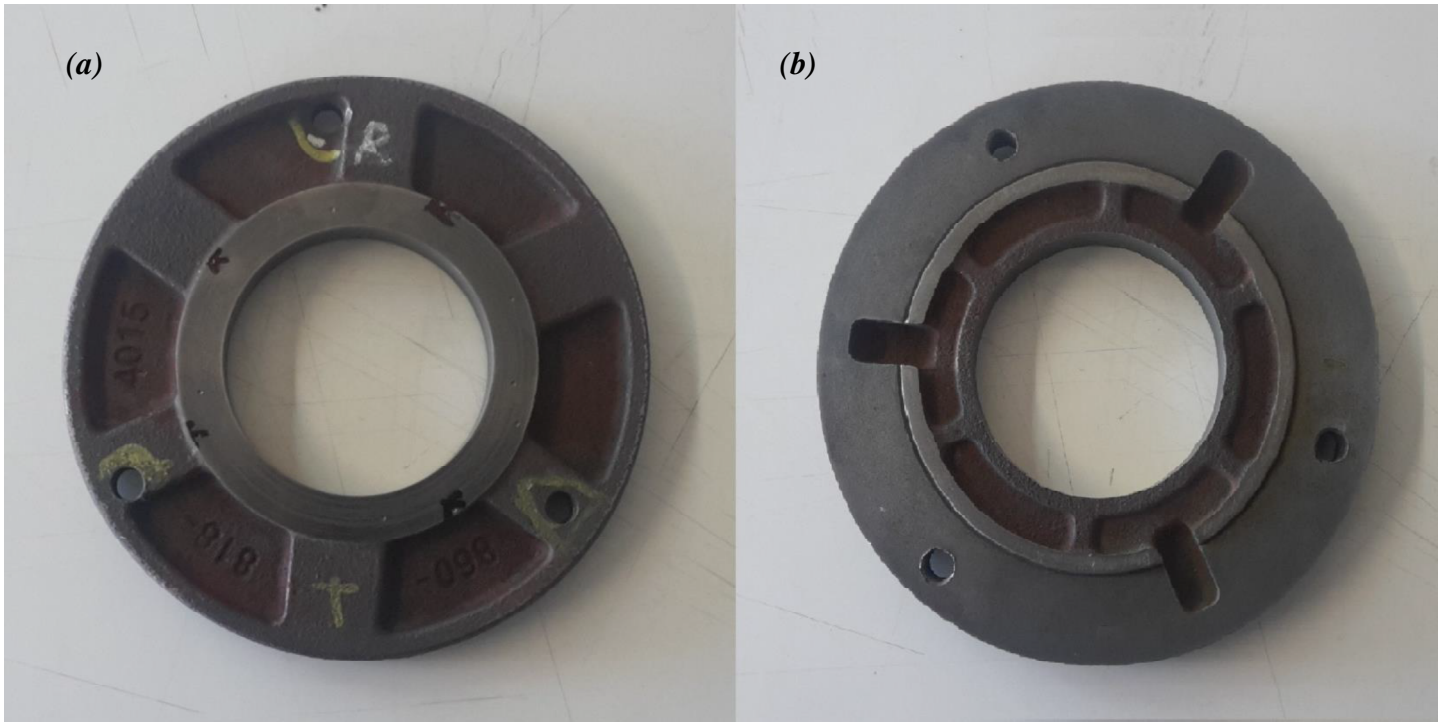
Photos des vues face frontale (a) et face dorsale (b) de la pièce étudiée
